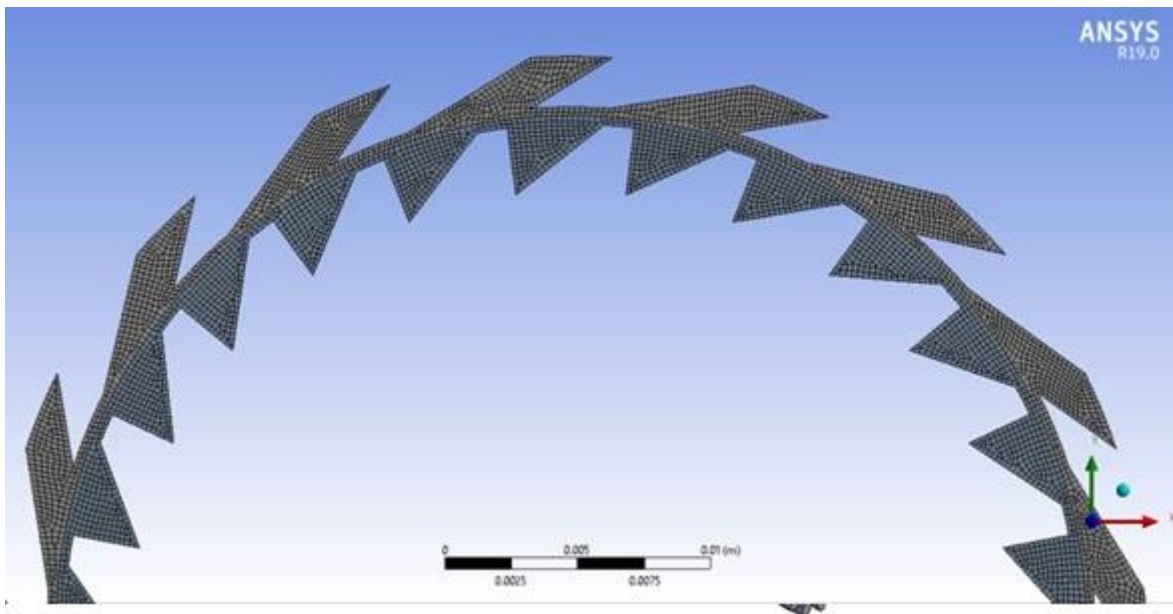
Diseño de la turbina motriz (rotor) en CAD
